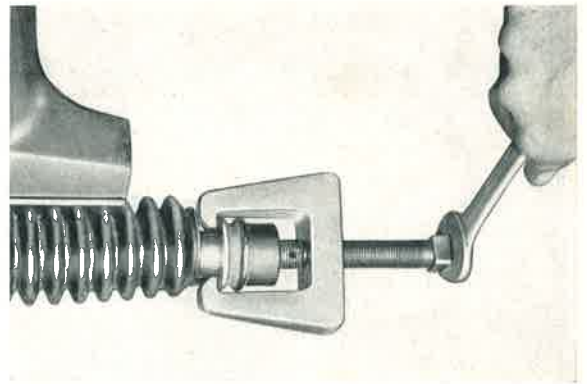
Die Lenkhebel beider Ausführungen werden mit dem gleichen Abzieher abgezogen, mit dem auch die Kugelbolzen der Spurstangen abgezogen werden.
